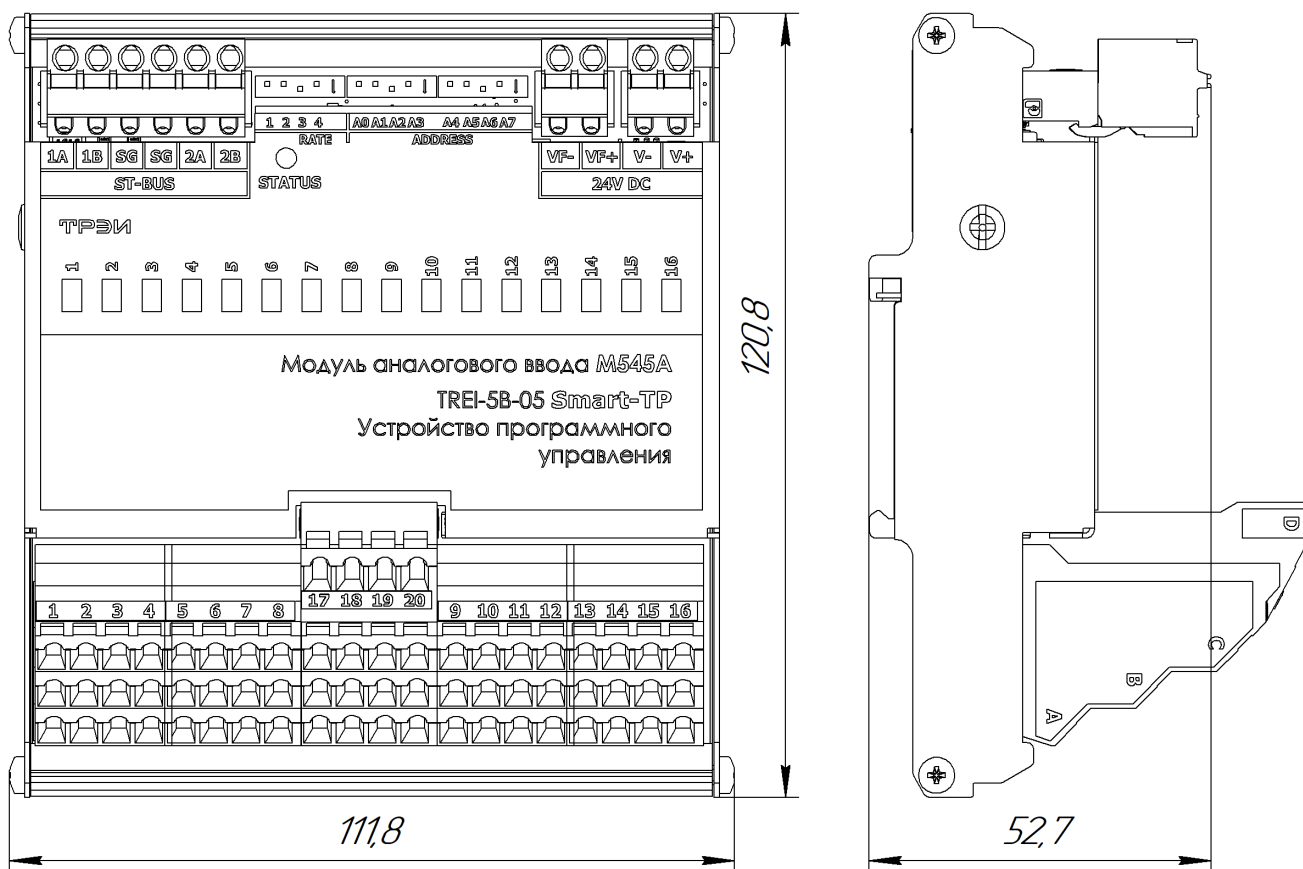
Чертеж общего вида M545A с указанием габаритных и присоединительных размеров
